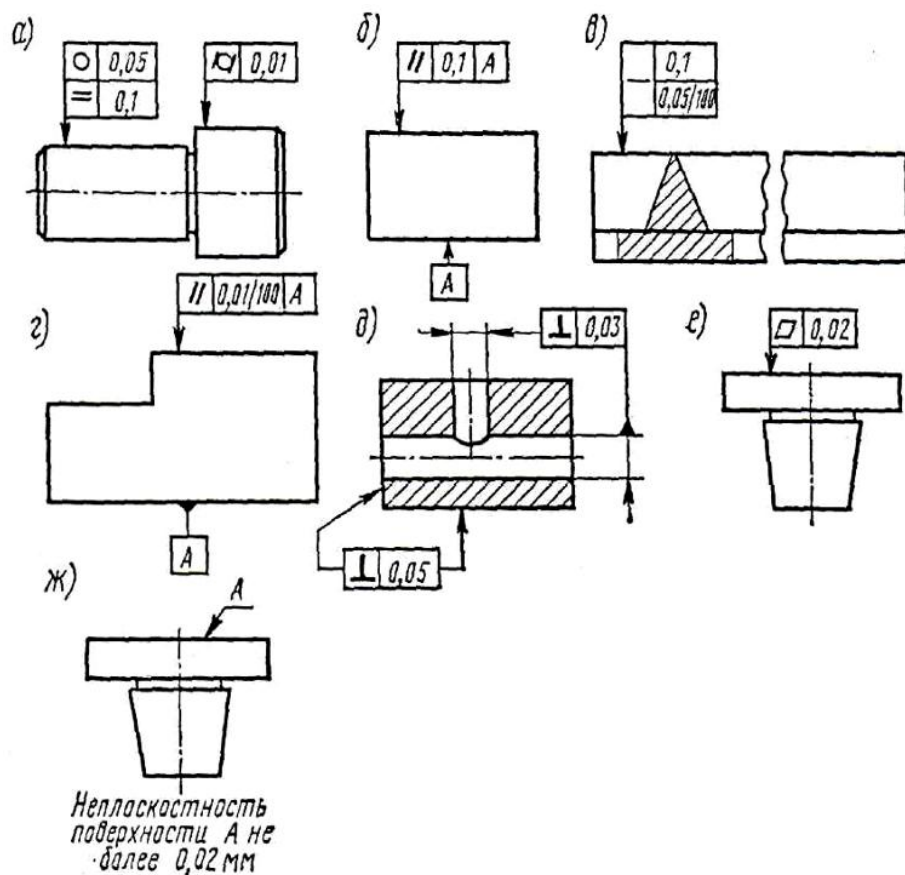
Условные обозначения на чертежах отклонений формы и взаимного расположения поверхностей деталей
